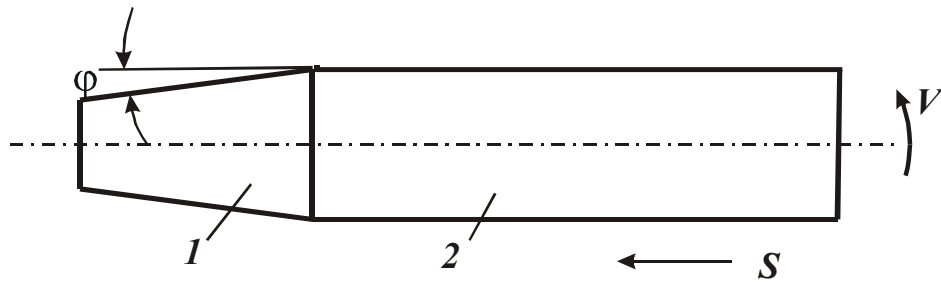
Принципова схема конструкції осевого багатолезового інструменту для обробки отвору: 1 – забірна частина; 2 – калібруюча частина
